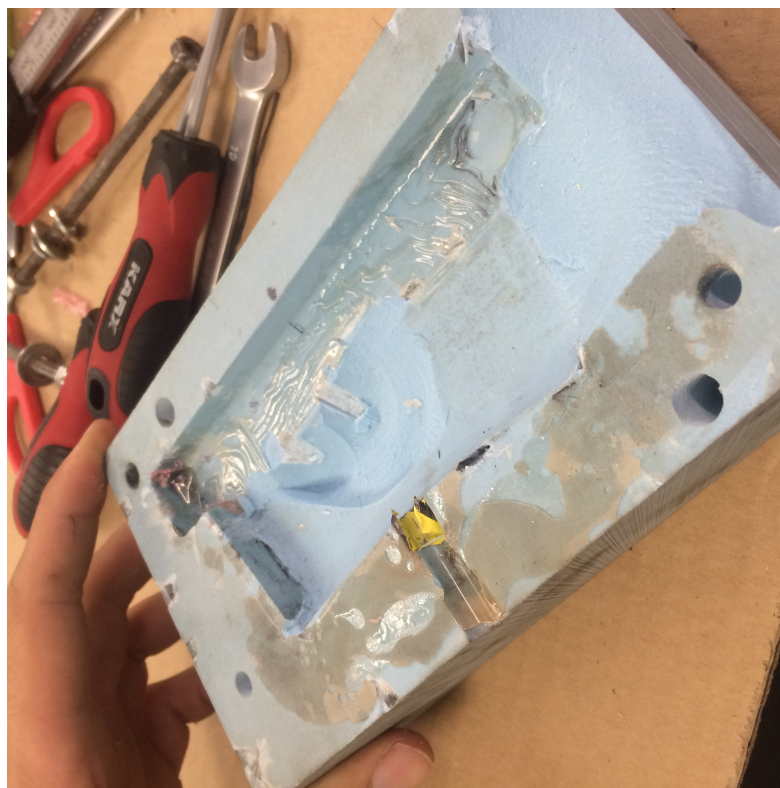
Fabricación II. Estado del molde tras el desmoldeo. (Fuente: Propia)
